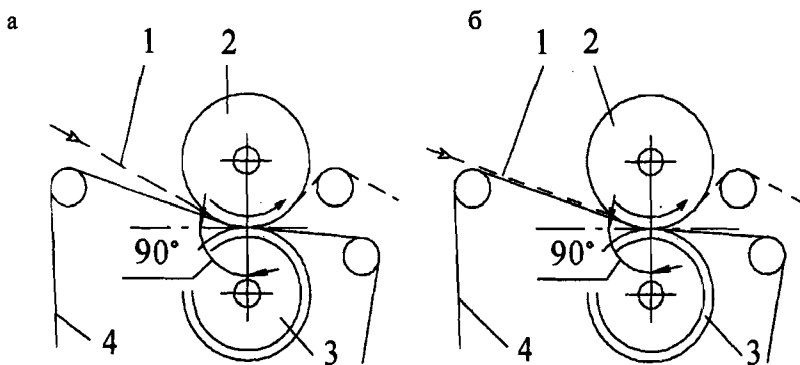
Заправка бумажного полотна в желобчатый пресс: 1 – бумажное полотно; 2 – верхний вал; 3 – желобчатый вал; 4 прессовое сукно
